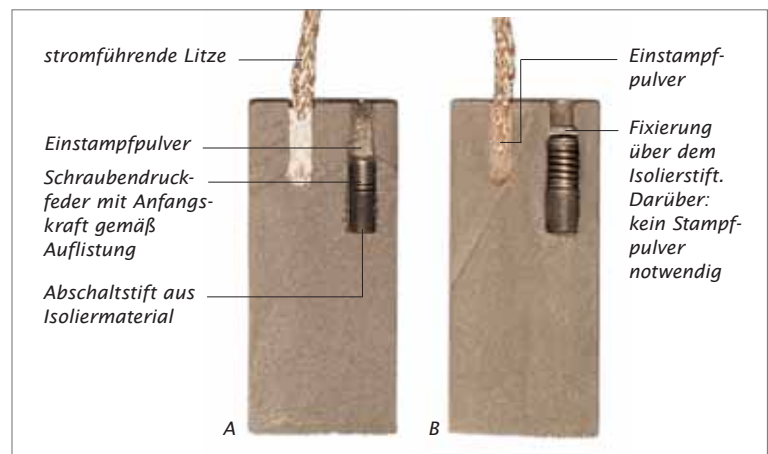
Spezielle Ausführung für Waschmaschinenmotoren.
